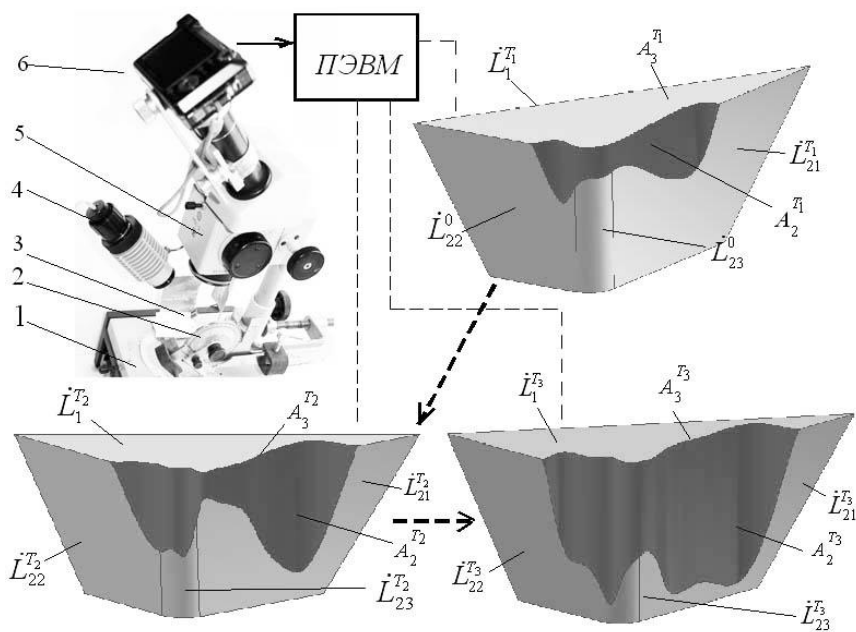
Пример формирования трех последовательных 3D-образов РЧ резца по результатам его контроля на стенде с бинокулярным микроскопом МБС – 9 (1 - корпус микроскопа, 2 – устройство поворота резца; 3 – контролируемый резец, 4 - система освещения; 5 – фотокамера
